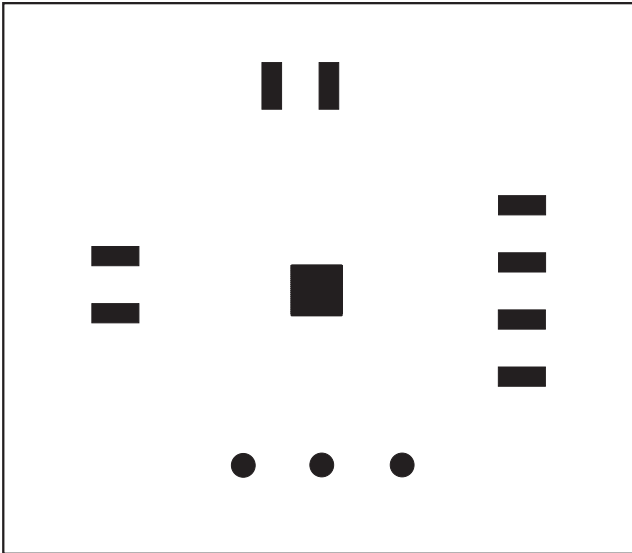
MAX2041 评估板PCB布局—底层阻焊层
